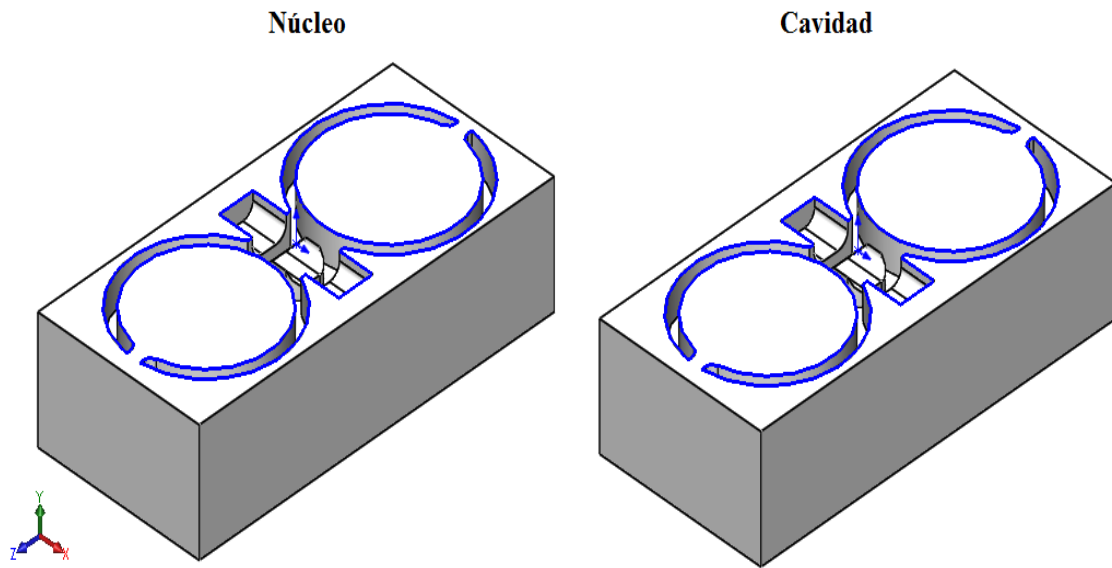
Moldes del núcleo y cavidad del acople de anillos
